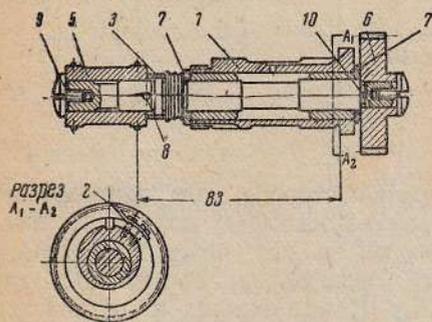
Внешний вид горизонтального вала: 1 — эксцентричный подшипник; 2 — маслосъемный щиток; 3 — кольцо; 4 — стопор; 5 — барабан; 6 — шестерня; 7 — шайба; 8 — штифт; 9 — винт; 10 — штифт
